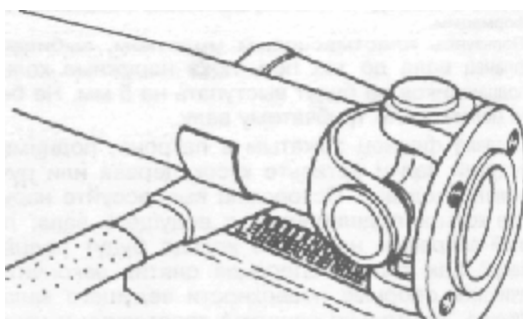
Когда под валом находится опора, с него можно выпрессовать наружные кольца подшипников
